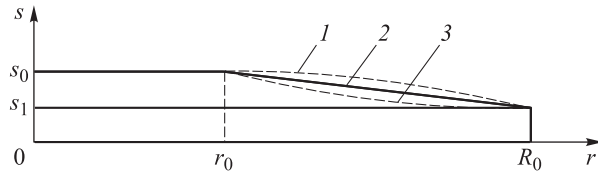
Схема заготовки переменной толщины: 1, 2 и 3 — соответственно выпуклая, прямолинейная и вогнутая образующие
